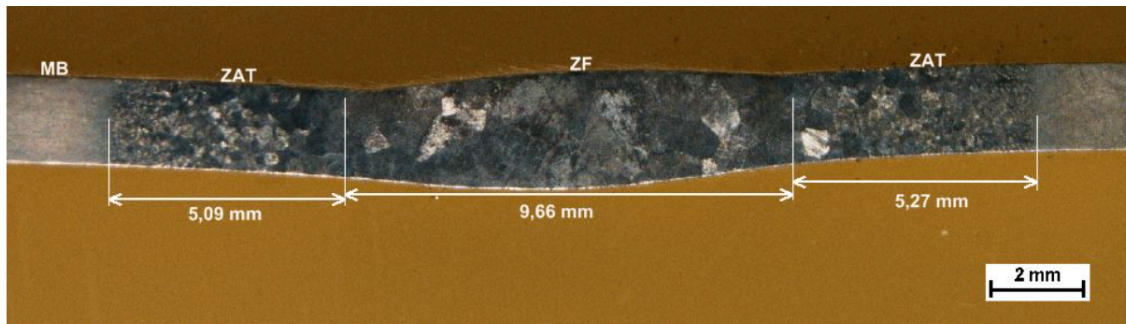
Macrographie d'une soudure avec un courant continu
